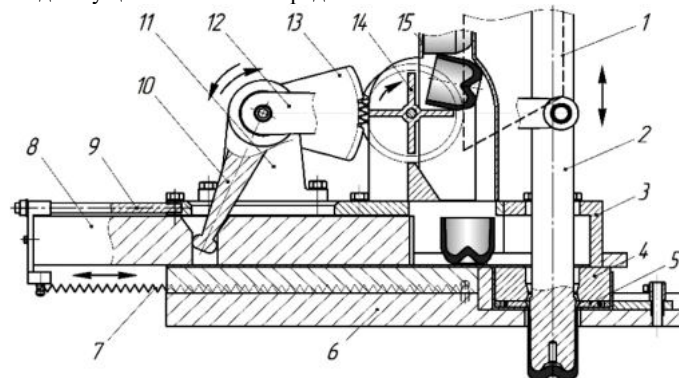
Конструкция шиберного питателя: 1 – нажимная пластина; 2 – пуансон; 3 – крышка; 4 – матрица; 5 – сьемник; 6 – основание; 7 – пружина; 8 – шибер; 9 – направляющая; 10, 12 – рычаги; 11 – кронштейн; 13 – зубчатая передача; 14 – отсекатель; 15 – лоток-магазин
